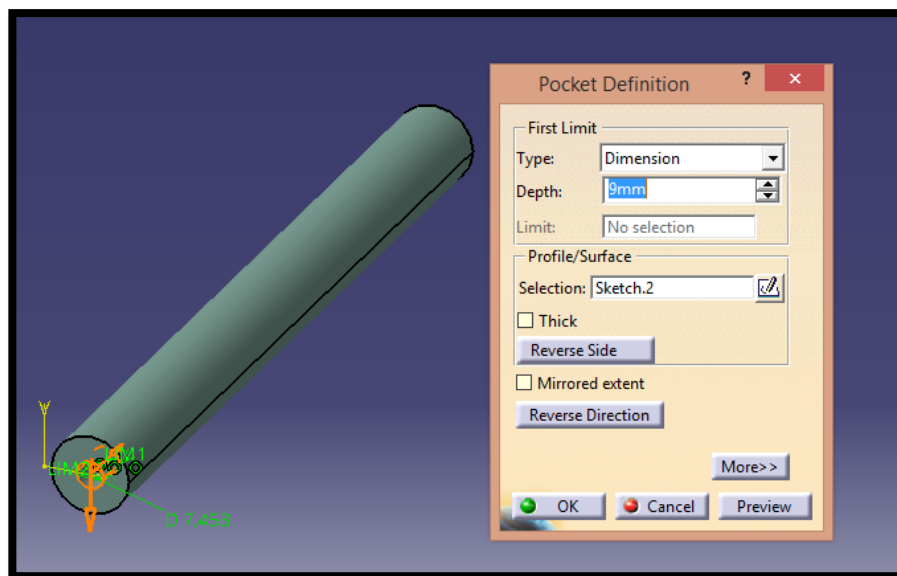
Seat mounting frame 11: Pocket barra superior
